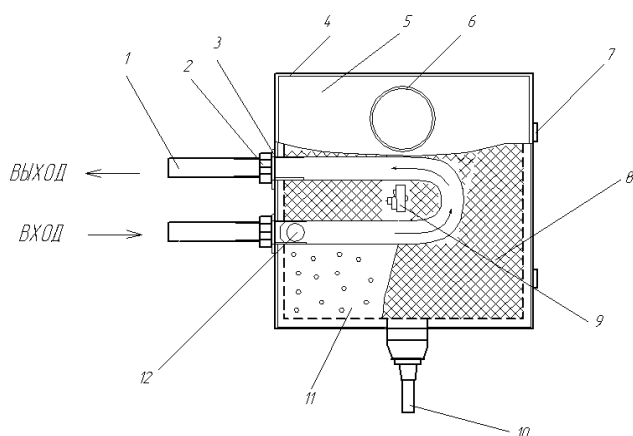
Принципиальная схема газоподогревателя ДВС: 1 – фигурный патрубок; 2 – гайка; 3 – уплотнительная шайба; 4 – корпус подогревателя; 5 – крышка подогревателя; 6 – патрубок горячего воздуха; 7 – шарнир крышки подогревателя; 8 – сетка инфракрасной горелки; 9 – кнопка пьезоподжига; 10 – штуцер для соединения с газовым редуктором; 11 – керамический нагревательный элемент
